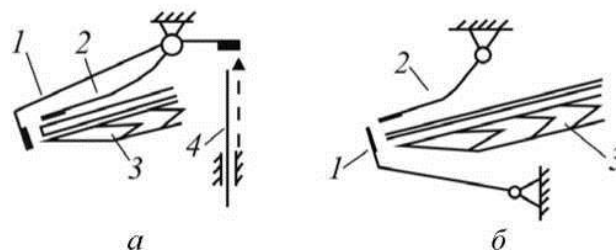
Схемы механизмов переднего выравнивания выстойного типа: а - с верхними упорами; б - с нижними упорами:
